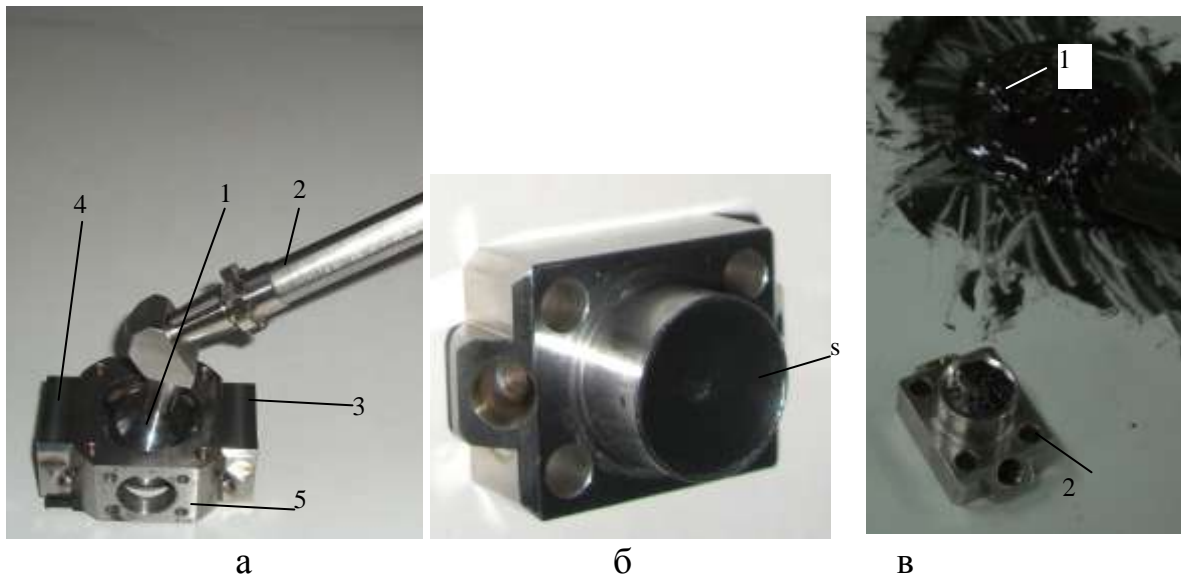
Сферичний шарнір ковзання (а), його вставки (б) із сферичною поверхню сформованою із феромагнітного металполімерного композиту та нанесення пастоподібного композита на поверхню вставки (в)
